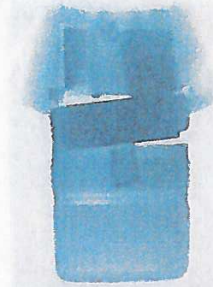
Röntgenfoto gemodificeerde schokbuis M6-H na de doorslagtest (Foto: KC W&M)
